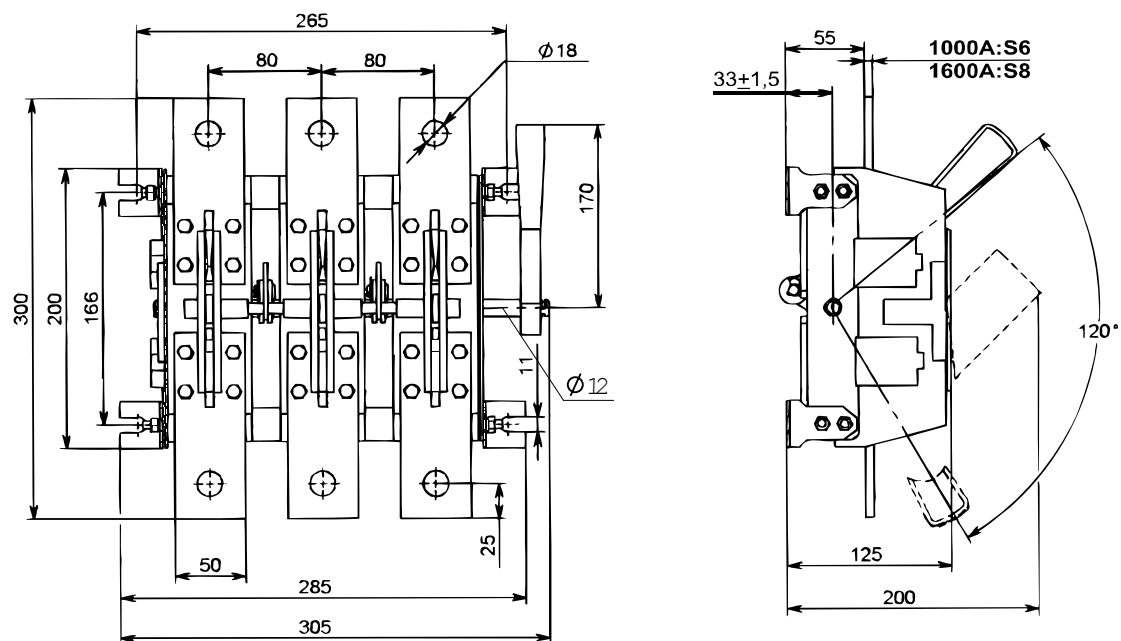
Разъединитель PE19-41(43)-31120-00 УХЛЗ с боковой рукояткой
